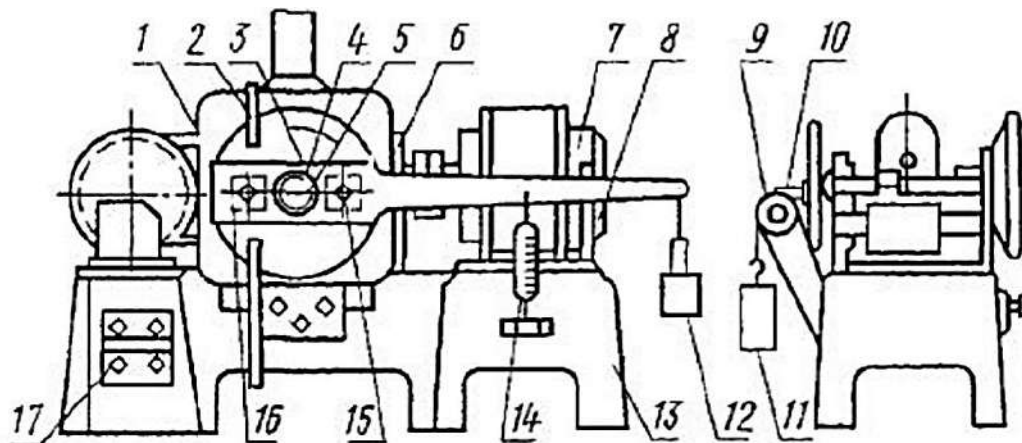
1 - кожух; 2 - воздуховод; 3 - неравноплечий рычаг; 4 - диск; 5 - полый вал; 6 - редуктор; 7 - электромотор; 8 - скоба; 9 - ролик; 10 - грузовой стержень; 11 - постоянный груз; 12 - уравнивающий груз; 13 - станина; 14 - динамометр; 15 - винты; 16 - рамка-держатель; 17-выключатель.
